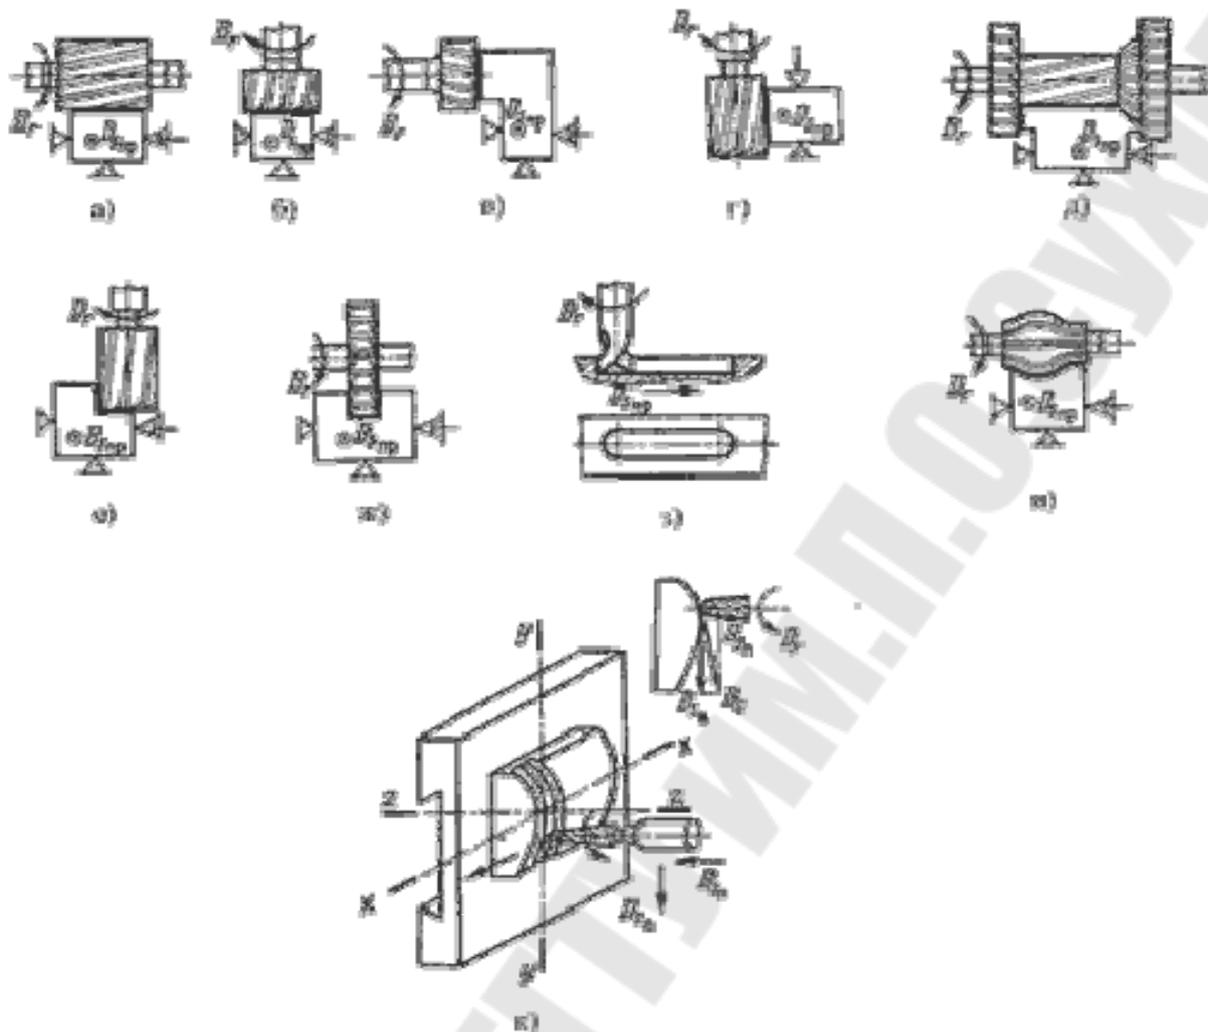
Схемы обработки заготовок на станках фрезерной группы.
